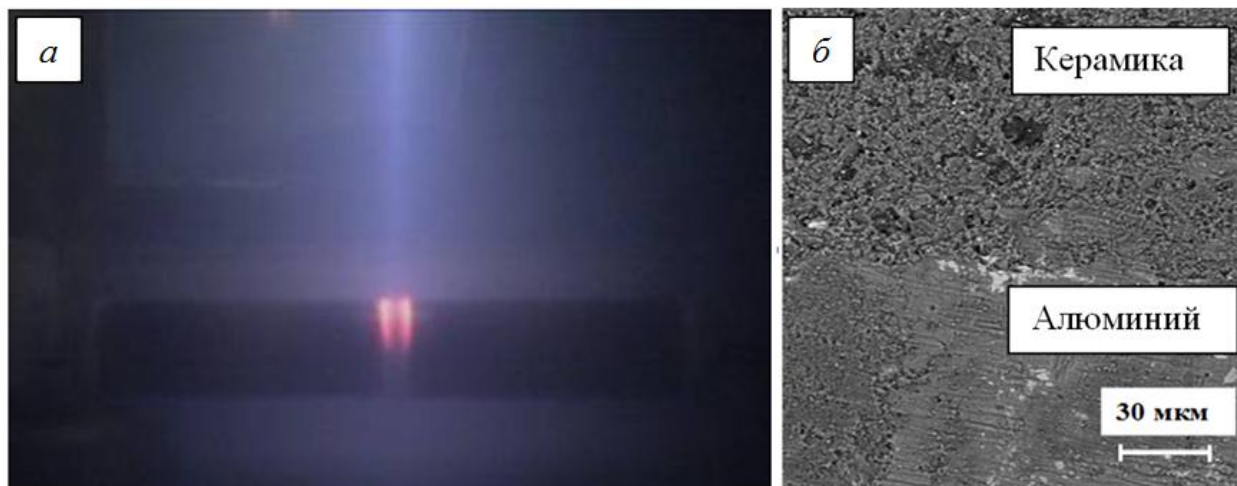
Фотография процесса сварки керамических труб (а), микрофотография шлифа места сварки керамики с алюминием (б)
